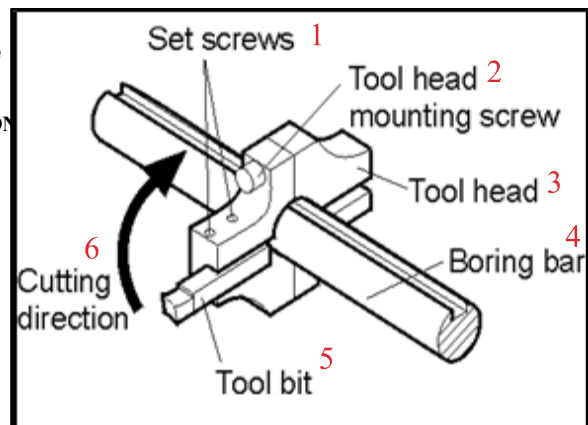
INSTALLATION DU PORTE-OUTIL
